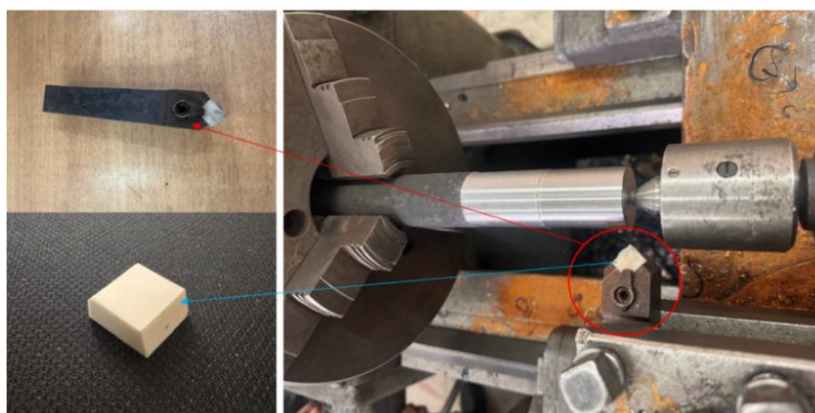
а-процесс крепления новых режущих пластин из минерального керамического композита к режущему инструменту токарного станка; б- процесс механической чистовой обработки поверхности закаленного стального вала
